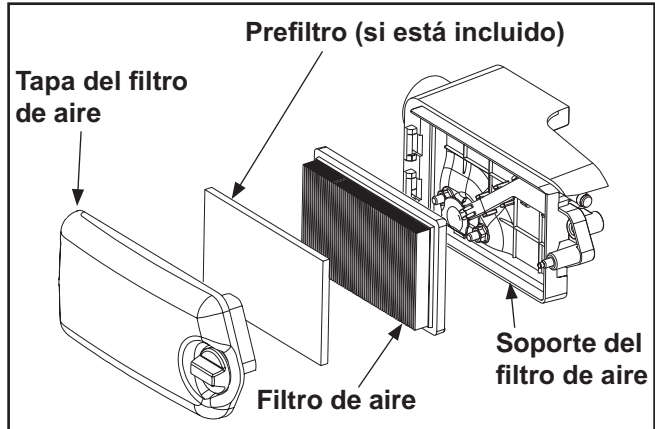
Conjunto de filtro de aire – Vista despiezada.
